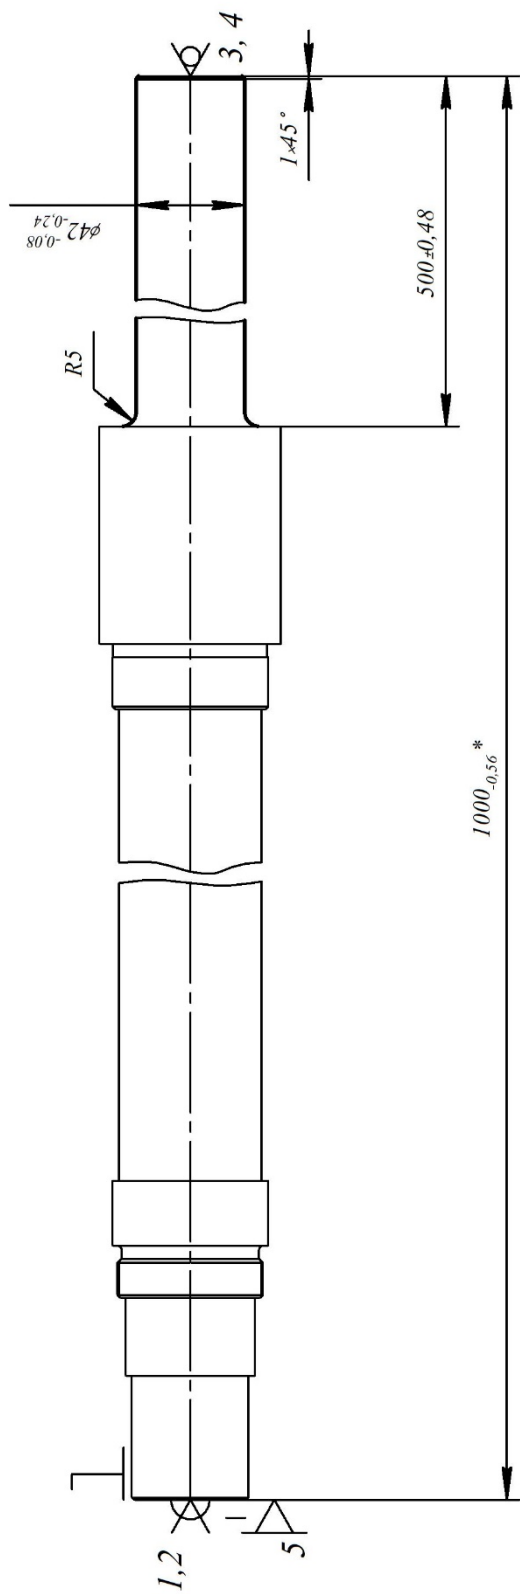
Схема базування заготовки на операції токарній 025, установ Б
